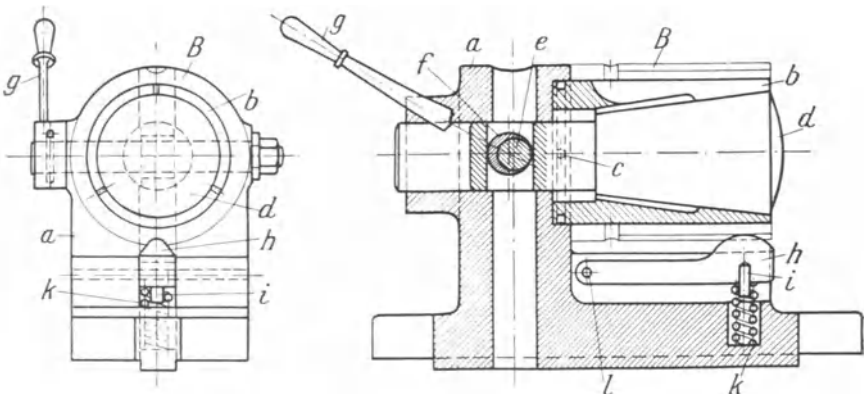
Fräsvorrichtung zum Nutenfräsen.
